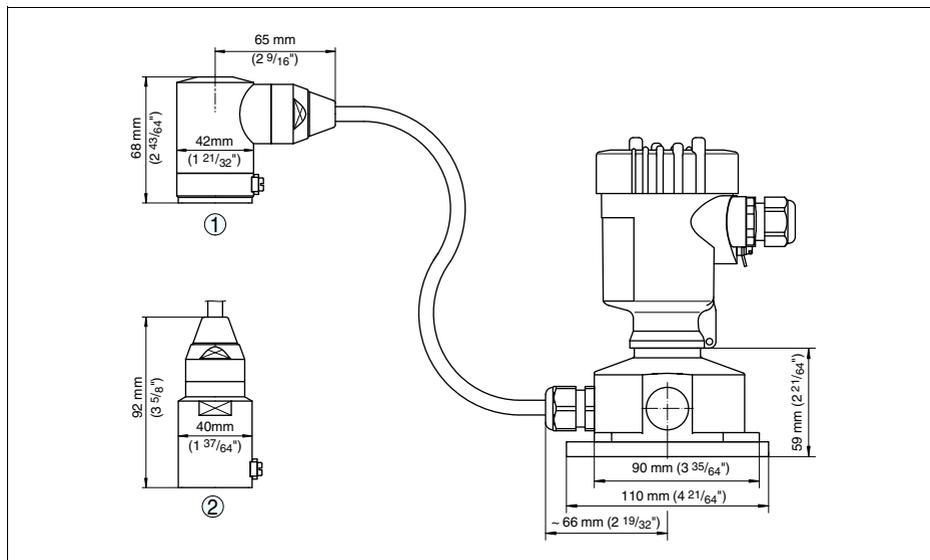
Исполнение IP 68 с выносным корпусом - без взрывозащиты
